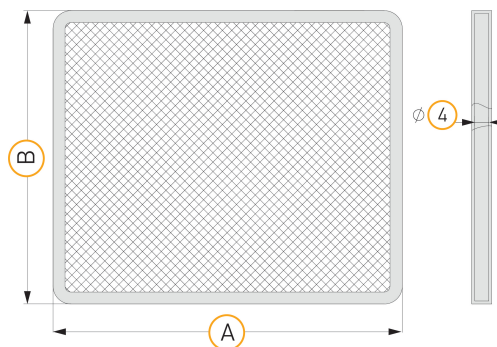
Внешний вид и основные размеры фильтрующих вставок SKF
